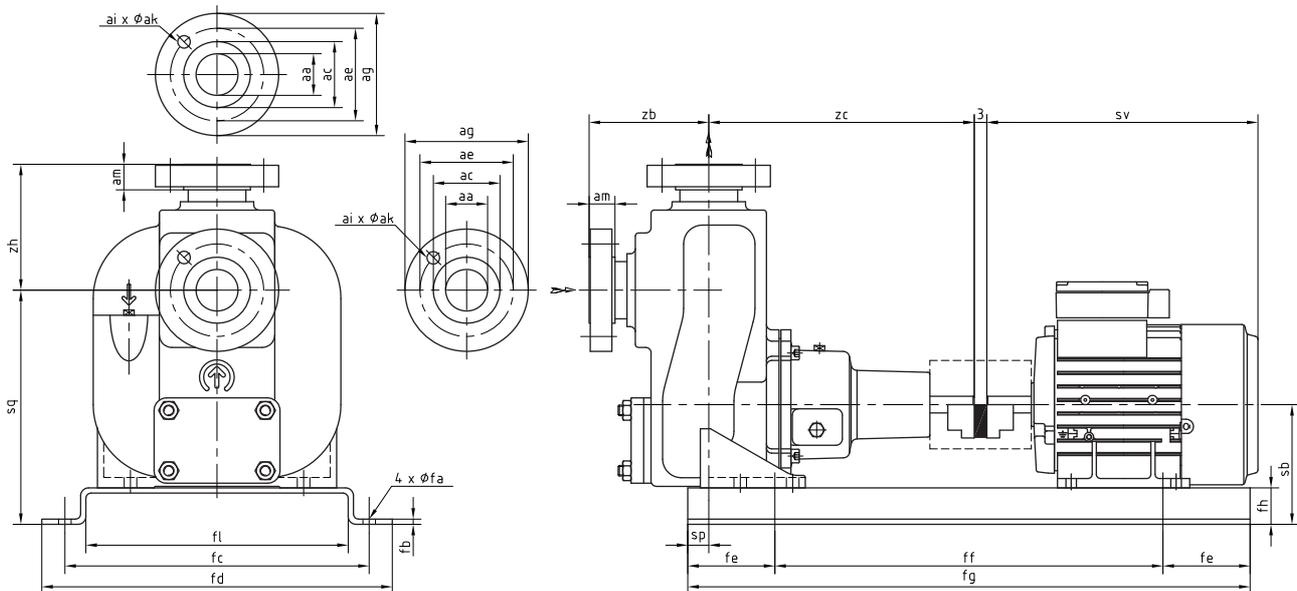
FRE - Pumpenaggregat A6, mit ISO 7005 PN20 Anschlüssen.
